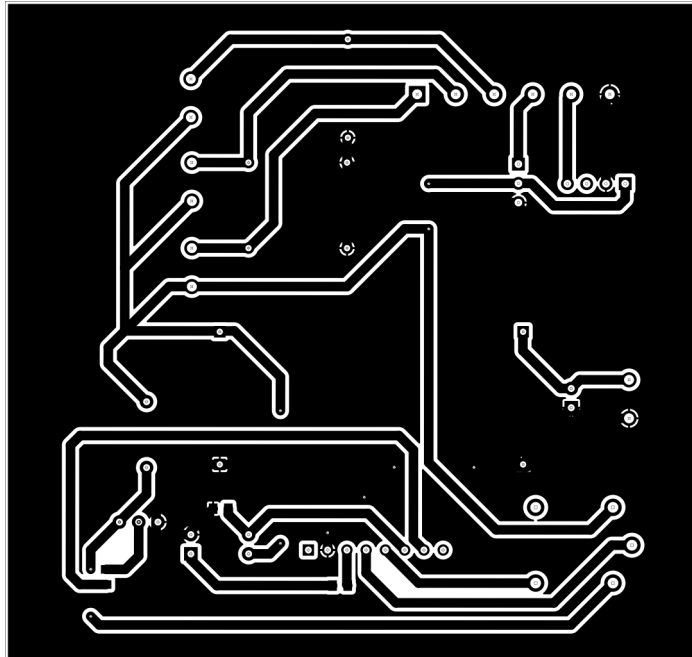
Trazado de rutas en la PCB. Fuente: Autores
